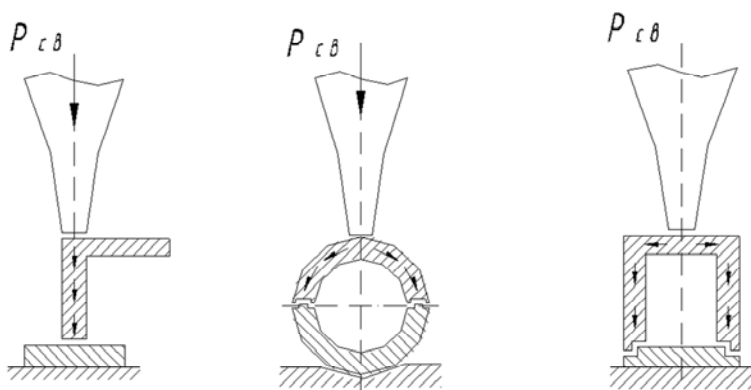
Схемы передаточной ультразвуковой сварки
